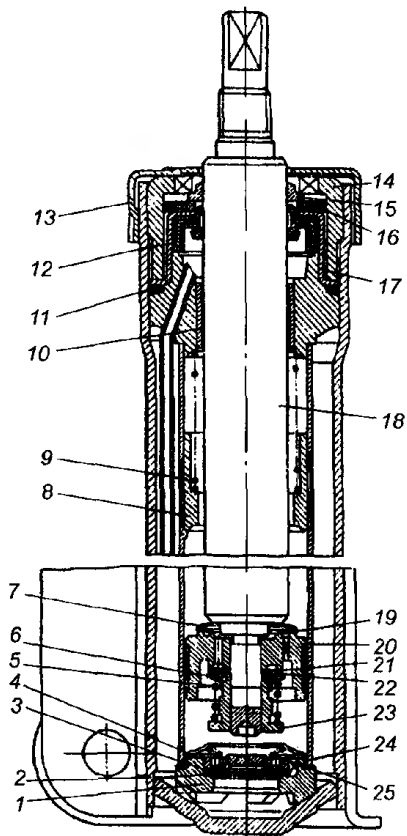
Телескопическая стойка: 1 – корпус клапана сжатия; 2 – диски клапана сжатия; 3 – дроссельный диск клапана сжатия; 4 – тарелка клапана сжатия; 5 – пружина; 6 – тарелка клапана отдачи; 7 – пружина перепускного клапана; 8 – плунжер; 9 – пружина плунжера; 10 – направляющая втулка штока со сливной трубкой; 11 – уплотнительное кольцо; 12 – уплотнительная манжета; 13 – опора буфера сжатия; 14 – гайка корпуса; 15 – защитное кольцо корпуса; 16 – уплотнительное кольцо резервуара; 17 – обойма уплотнительной манжеты; 18 – шток; 19 – тарелка перепускного клапана; 20 – поршень с кольцом; 21 – дроссельный диск клапана отдачи; 22 – диски клапана отдачи; 23 – гайка клапана отдачи; 24 – обойма клапана сжатия; 25 – пружина.
